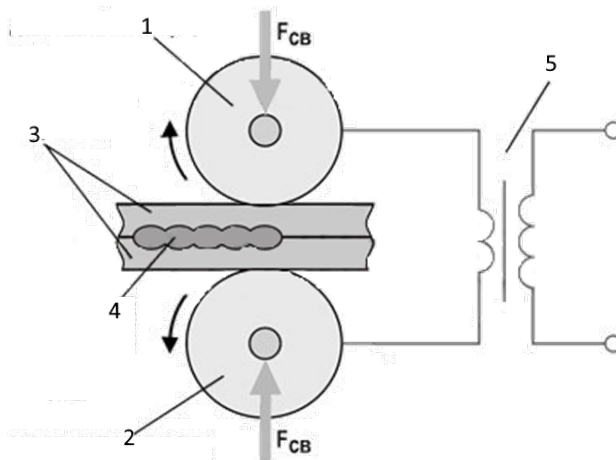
Схема контактной роликовой сварки:
